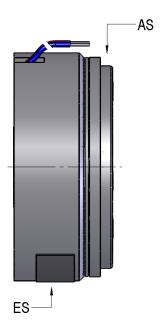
/1: High Torque Bremse Typen 86 611..P00 mit Anker 800
